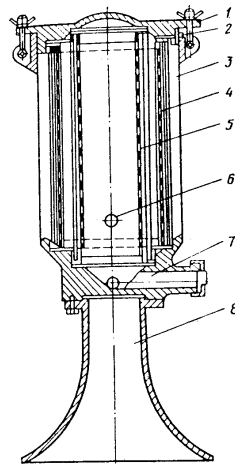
Циліндричний фільтр: 1 – кришка; 2 – гумова прокладка; 3 – корпус; 4 – зовнішня сітка; 5 – внутрішня сітка; 6 – патрубок, що відводить; 7 – патрубок, що підводить; 8 – підставка
